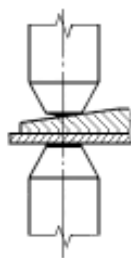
Eixo de soldadura não perpendicular com chapa
